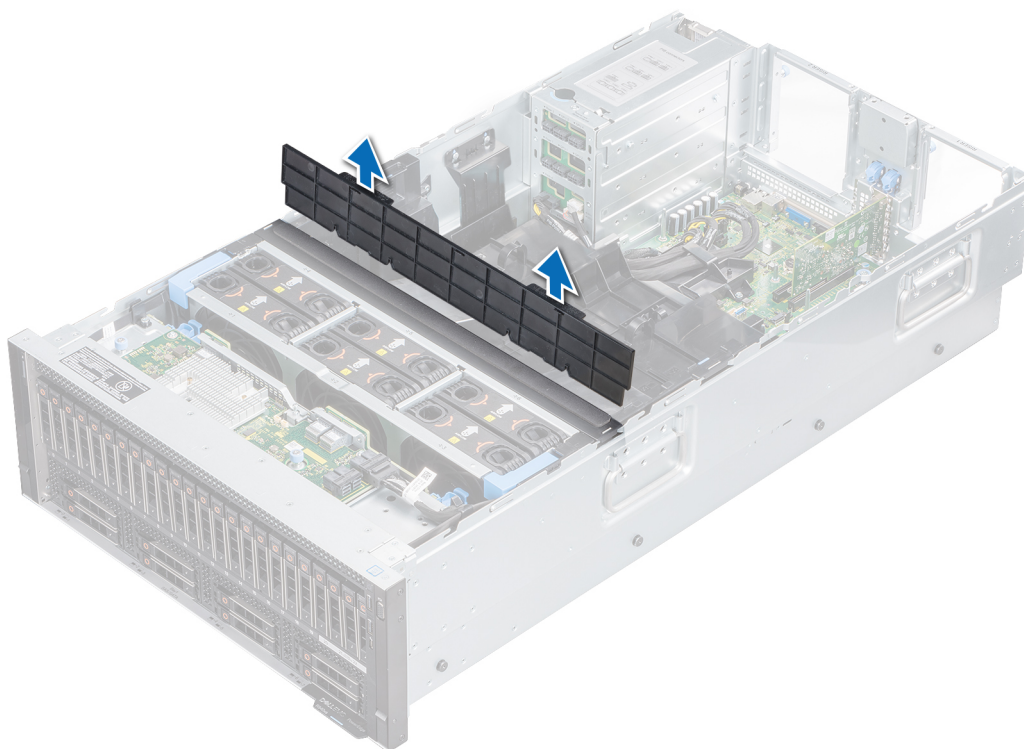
Entfernen des GPU-Kühlgehäuses
